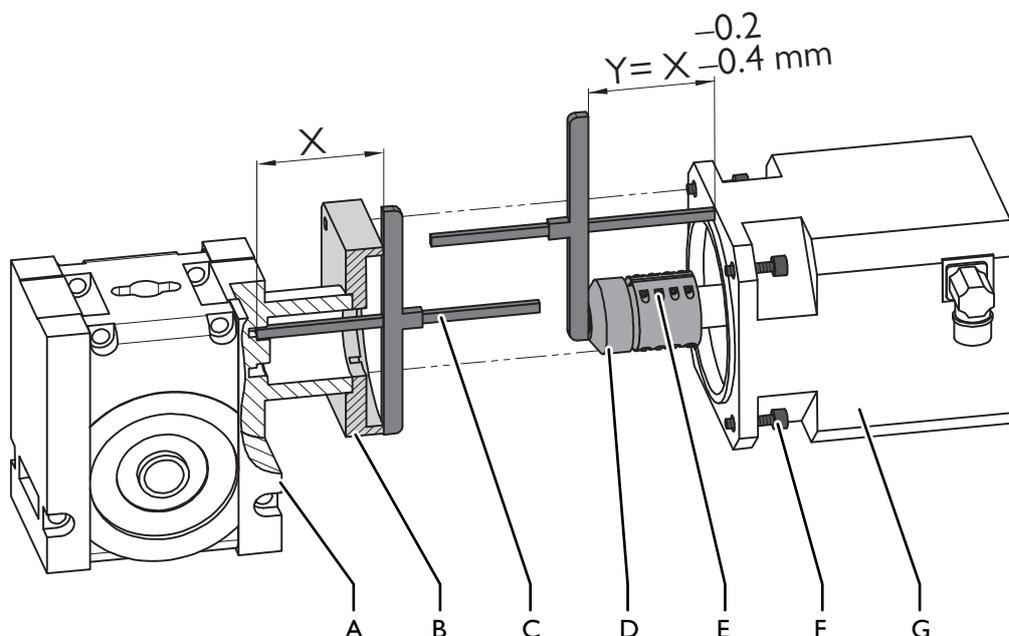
Posicionar o acoplamento sobre o eixo do motor
